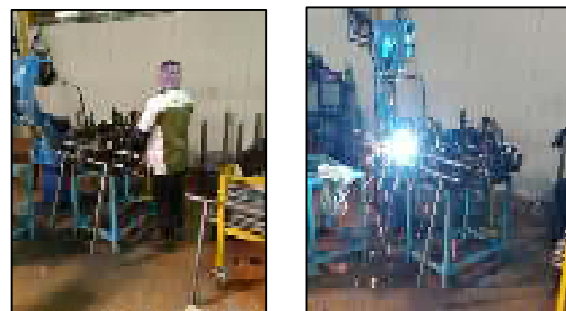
Optimasi Desain *Welding Jig* Pengangkat Bawah
